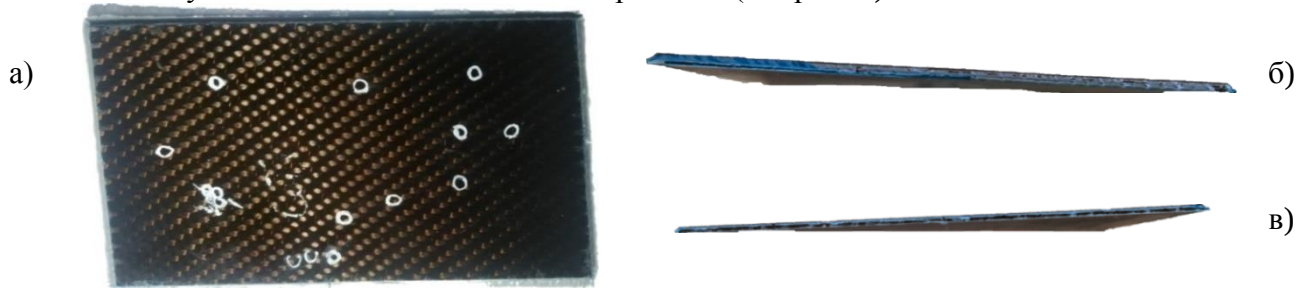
Деформированный образец: а) вид сверху, б) сбоку, в) спереди
